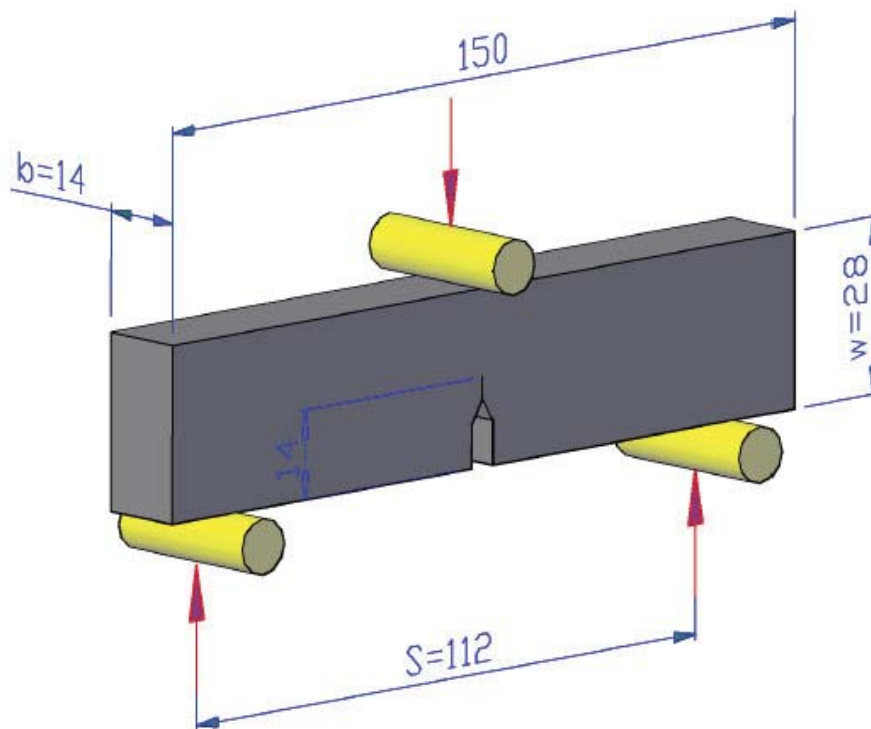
Corpos de prova SE (B) – Dimensões padrões finais para o ensaio.
